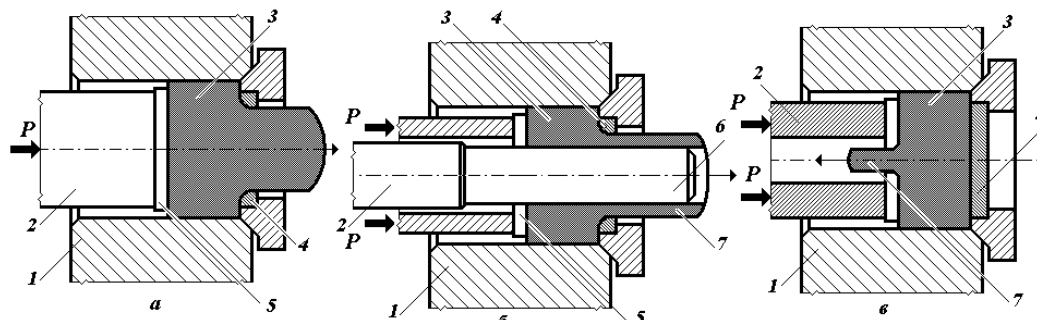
Схемы прессования: а - прямое прессование сплошного профиля; б - прямое прессование полого профиля; в - обратное прессование сплошного профиля; 1 - контейнер; 2 - пуансон; 3 - заготовка; 4 - матрица; 5 - пресс-шайба; 6- игла; 7 - прессованное изделие; P – усилие прессования
